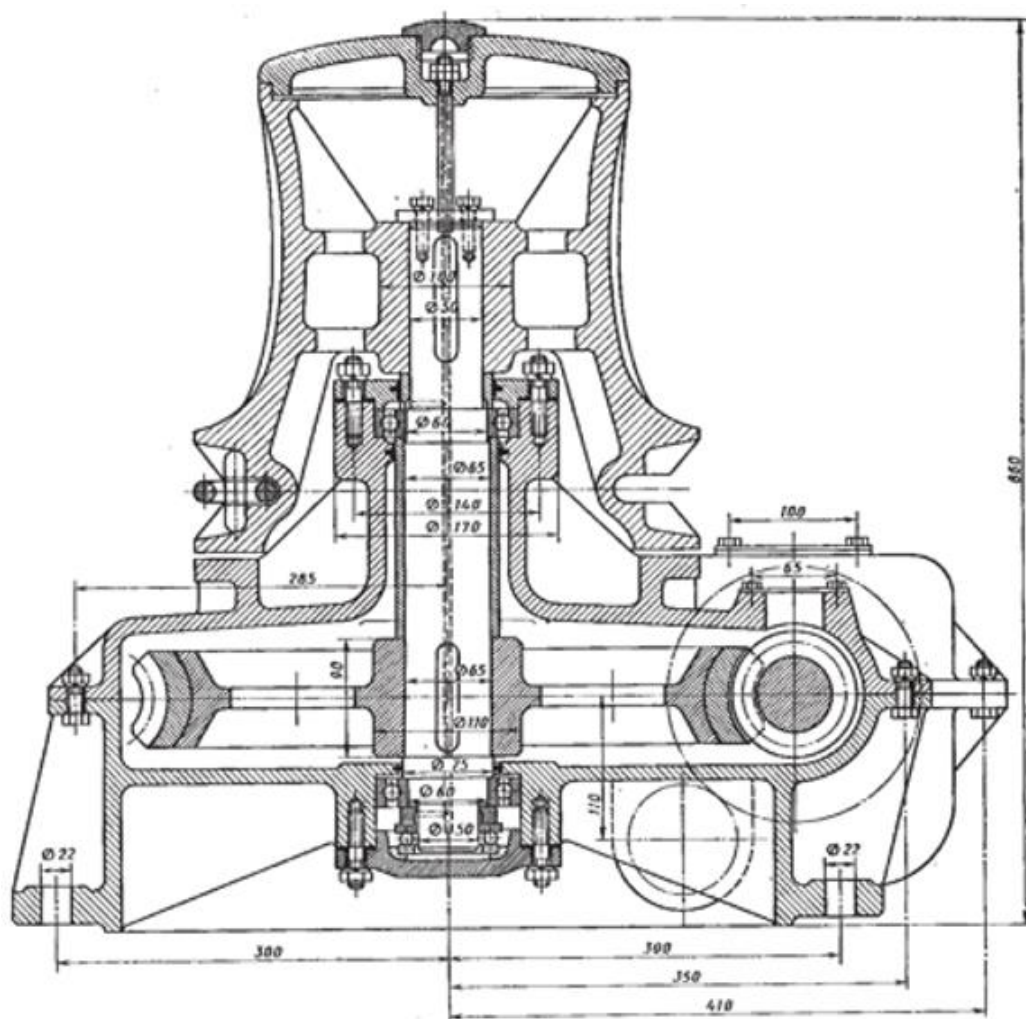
Пример конструкции автомобильного штока с вертикальным валом
